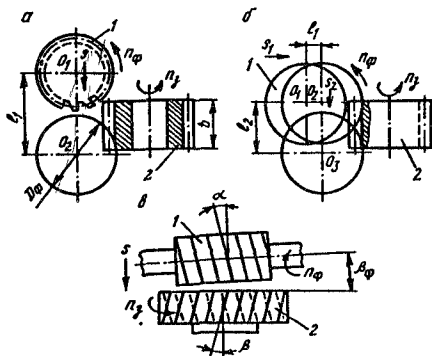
Схемы фрезерования зубьев цилиндрических колес червячной модульной фрезой
